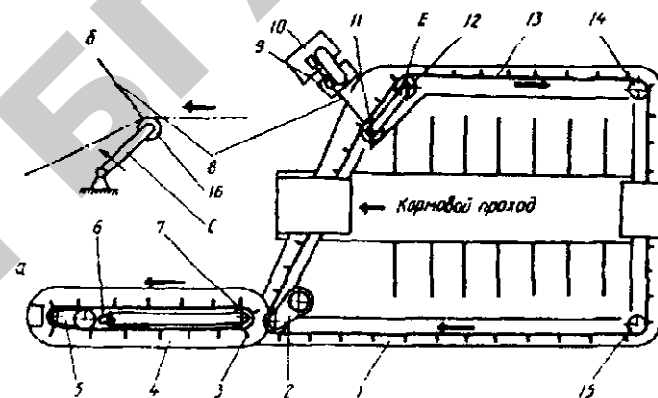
Скребковый навозоуборочный транспортер ТСН-160А:
